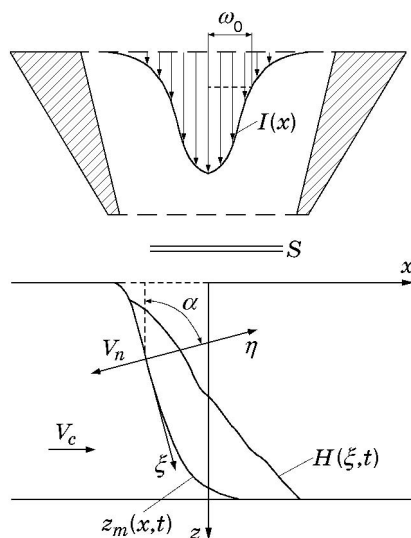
Схема взаимодействия лазерного луча и струи газа с поверхностью металлической пластины и слоем расплава
